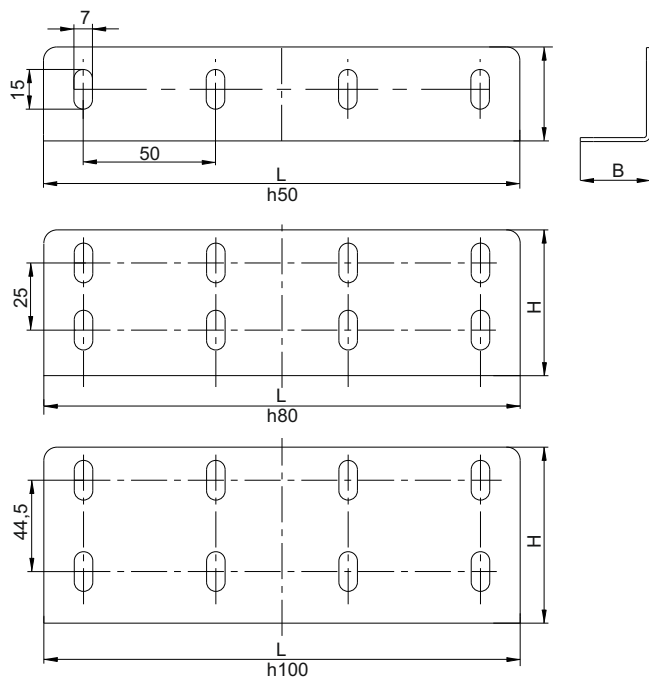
Пластина соединительная усиленная / Figure 2 – Reinforced connecting plate
